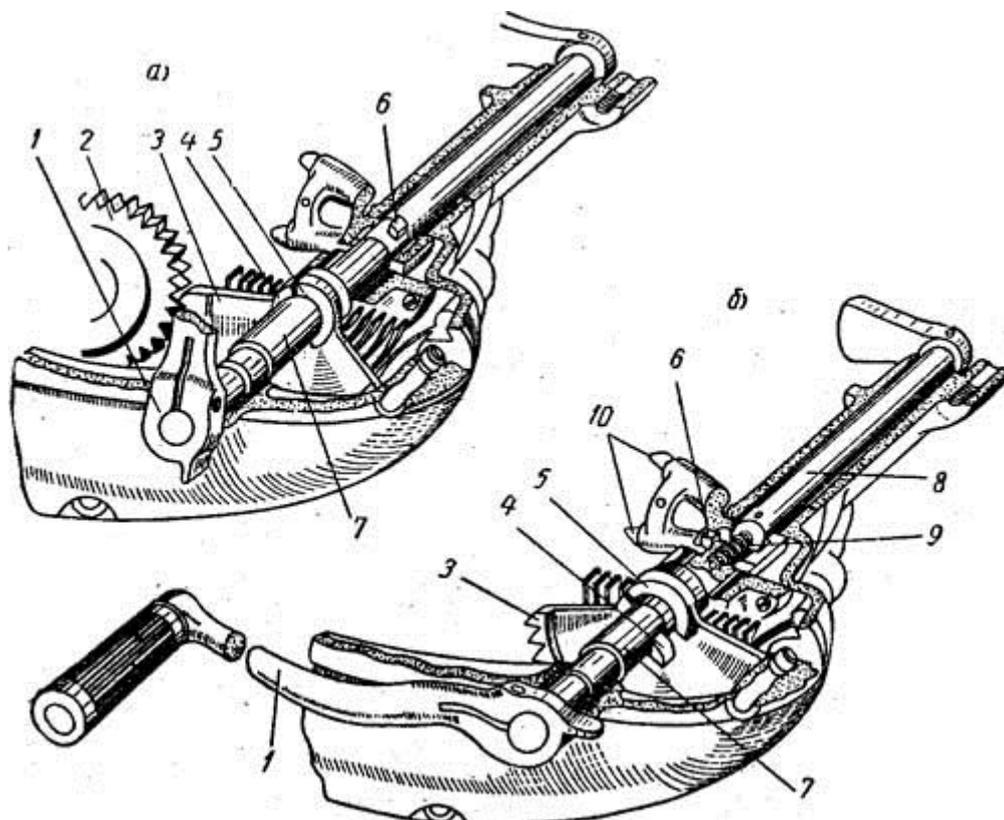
Положение деталей пускового механизма и механизма переключения передач: а - при запуске двигателя, б - при переключении передач. 1 - рычаг; 2 - храповая шестерня пускового механизма; 3 - сектор плюсового механизма; 4 - шлиц для привода пускового механизма; 5 - выступ на секторе пускового механизма; 6 - шлиц для привода механизма переключения передач; 7 - вал рычага; 8 - вал механизма переключения передач; 9 - пружина; 10 - собачки вала механизма переключения передач
